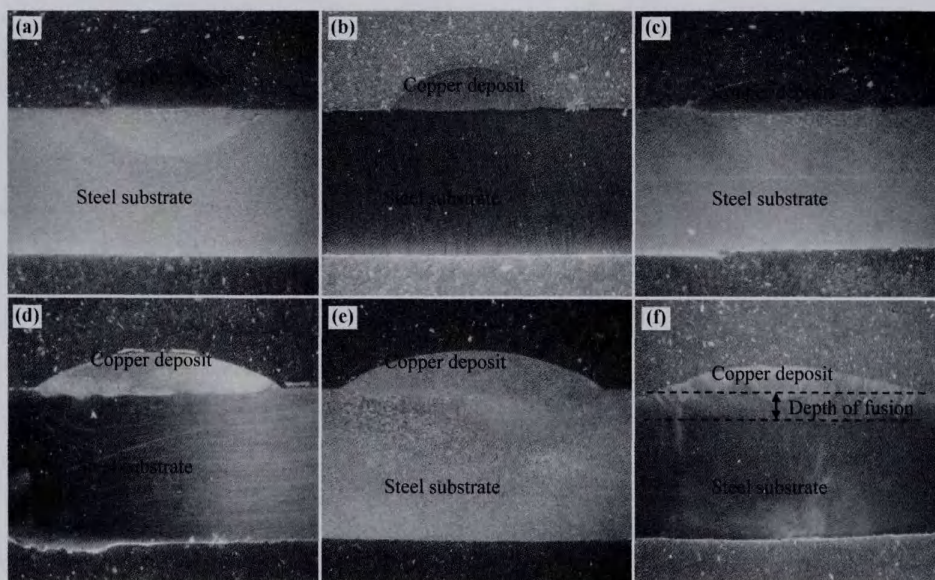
不同焊接参数下的堆焊接头截面形貌
